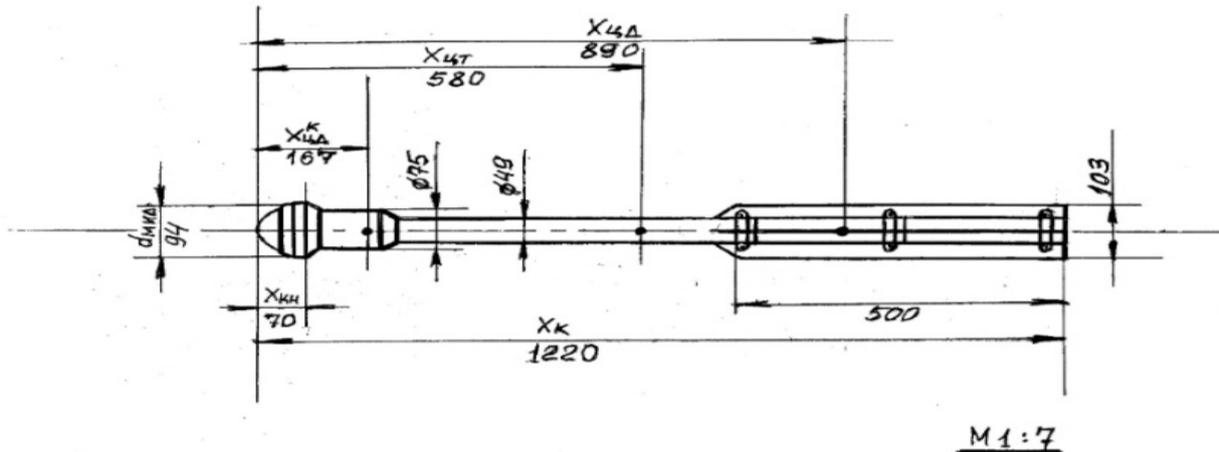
Чертеж корпуса ракеты и положение её центра тяжести [2]
